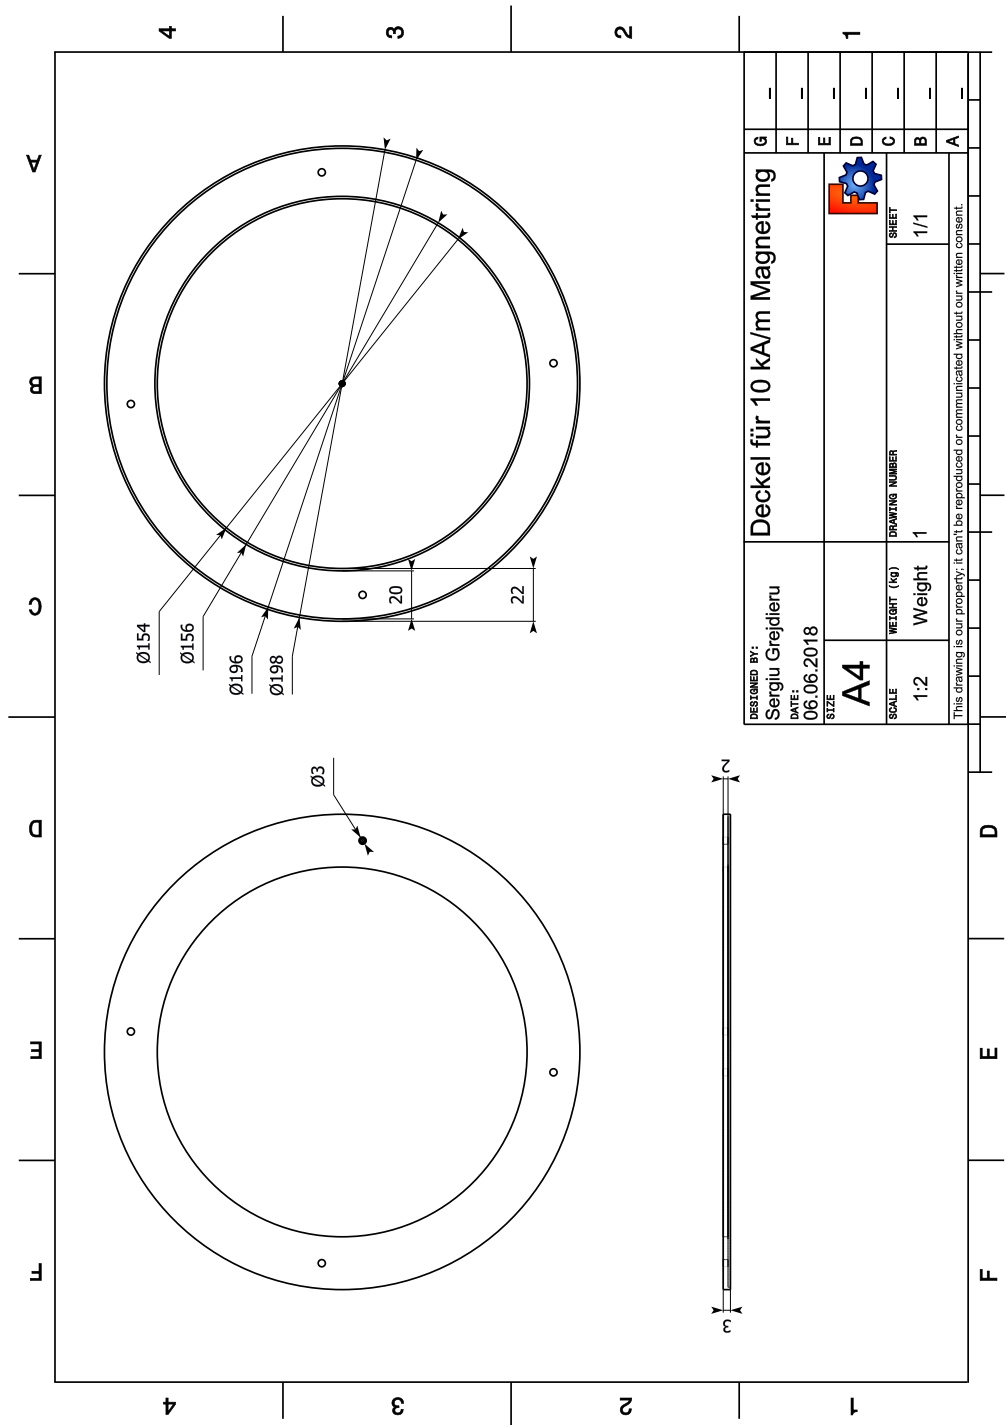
Technische Zeichnung: Deckel für Magnetring 10 kA/m
